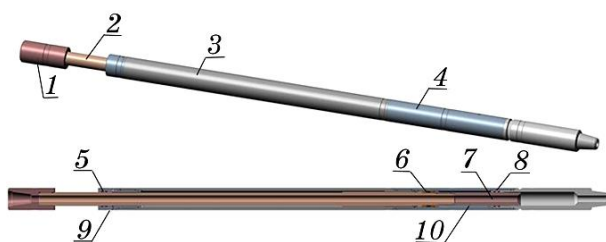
Інтенсифікатор яса: 1 — перехідник, 2 — шток, 3 — корпус верхній, 4 — корпус нижній, 5 і 8 — ущільнювач штока, 6 — ущільнювач циліндра, 7 і 9 — заглушка, 10 — хвостовик штока.
